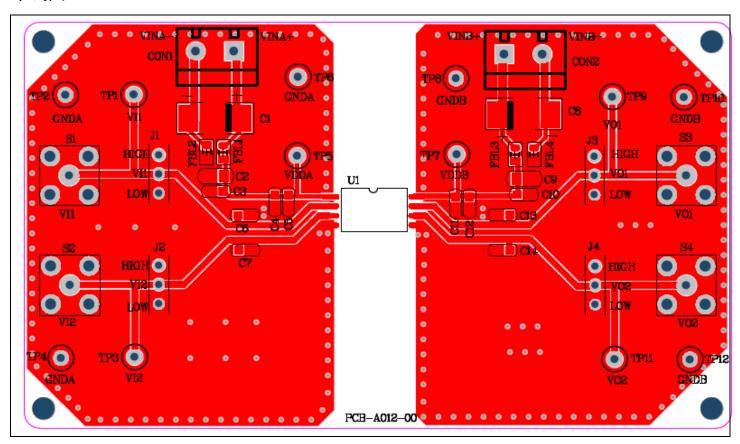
CA-IS372x SOIC8-G PCB 的 3D 仿真图
